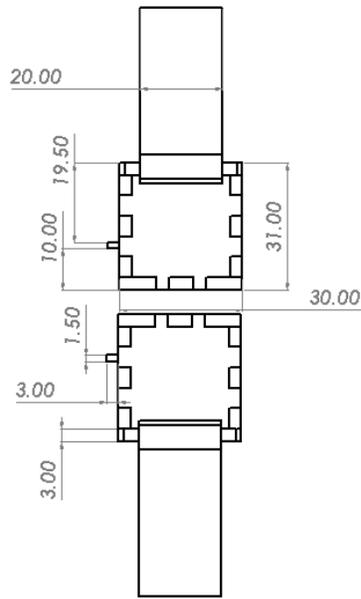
Planos vista lateral del dispositivo vibrador final.
